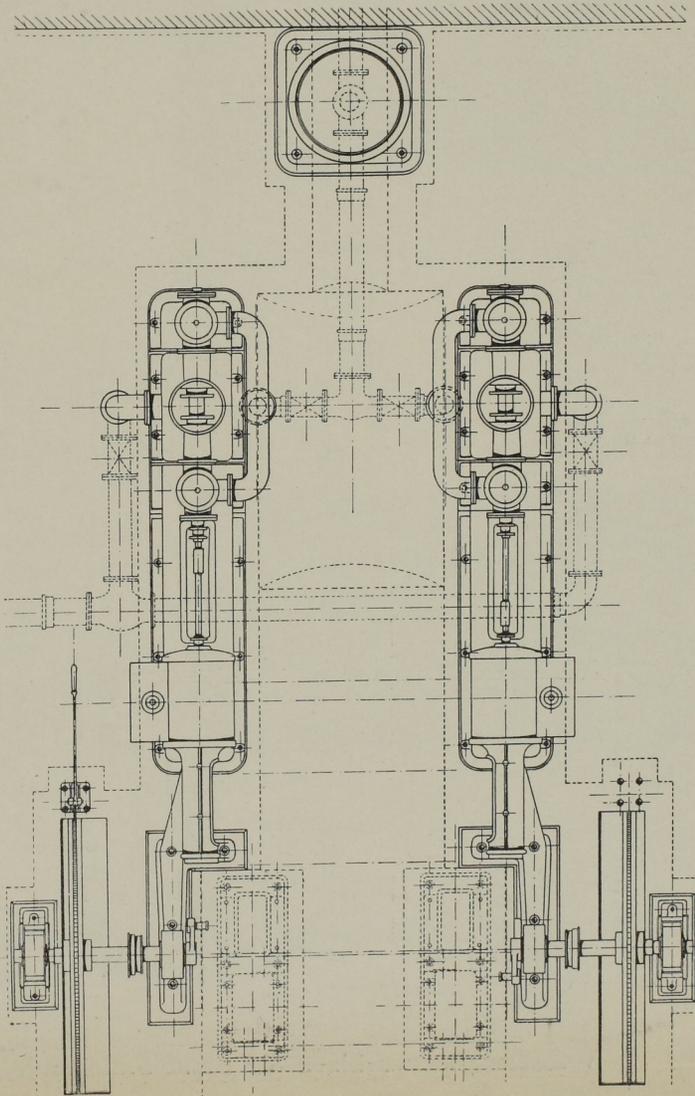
Grundriss der Pumpmaschine. Masst. 1 : 75.
